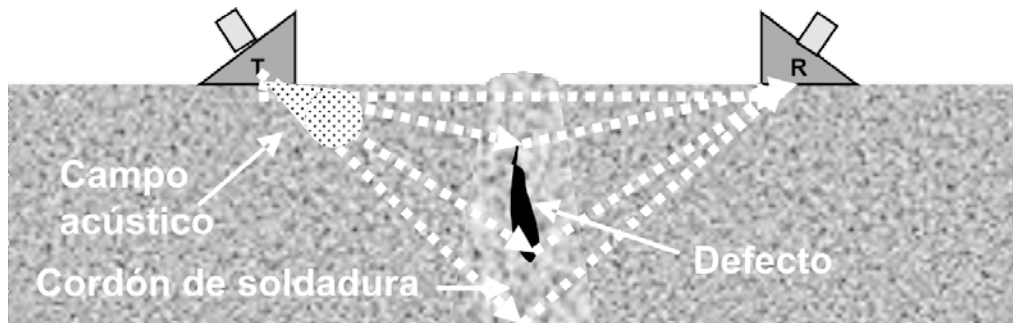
Principio básico para la configuración de la técnica TOFD. Se muestra la sección transversal de una probeta compuesta por dos láminas de acero soldadas y un defecto embebido en el cordón de soldadura
